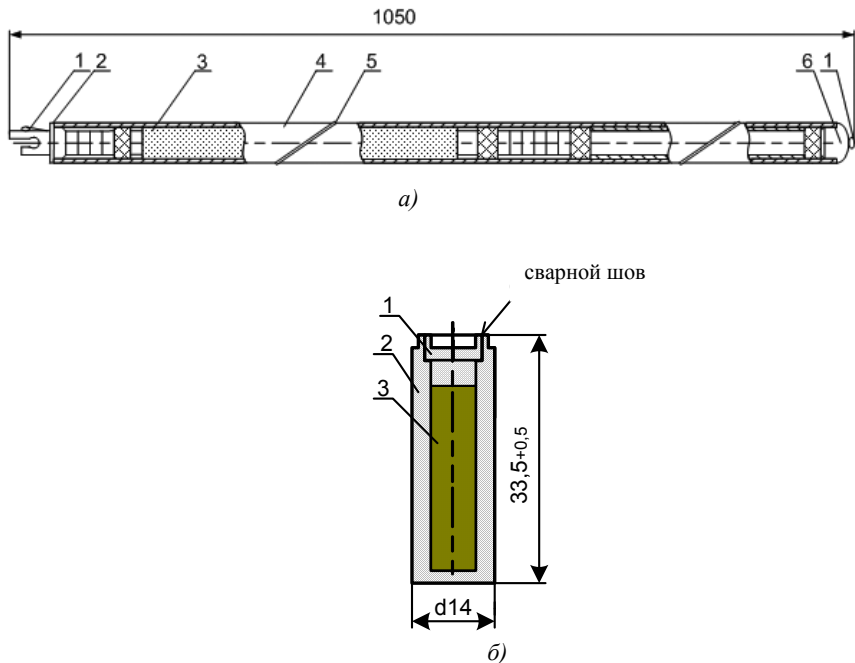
Примеры конструкций изделий АЗ ядерных реакторов: а) конструкция твэла: 1 – узел крепления дистанционирующей проволоки; 2, 6 – верхнее и нижнее сварные соединения оболочки с заглушками; 3 – топливный сердечник; 4 – оболочка; 5 – дистанционирующая проволока; б) конструкция типового ИИИ: 1 – заглушка (крышка); 2 – оболочка (корпус); 3 – сердечник (активная часть)
